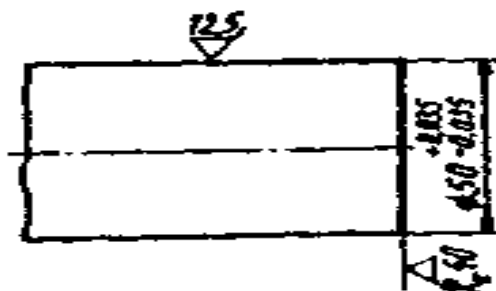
Обозначение отклонений и шероховатости на чертеже
